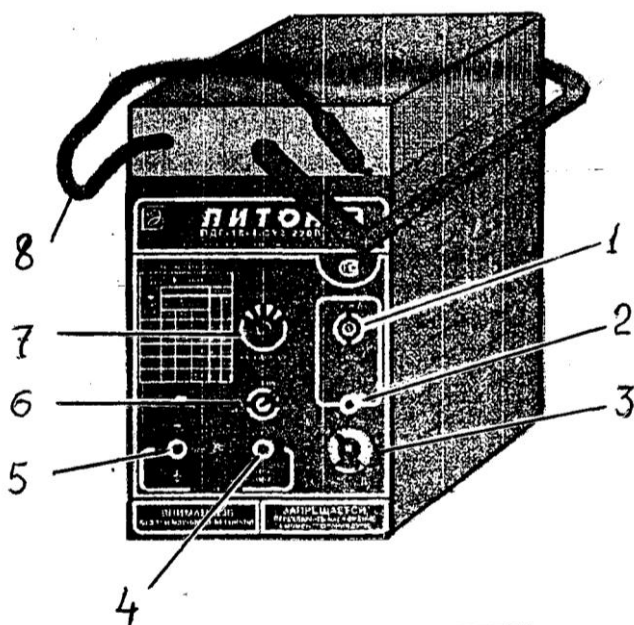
Источник питания для полуавтоматической сварки в среде углекислого газа:
